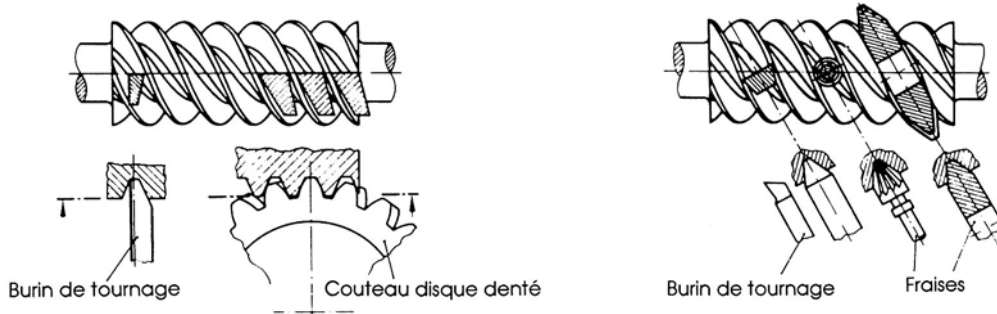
Définition et fabrication des flancs de la vis : vis de type ZA et ZN
